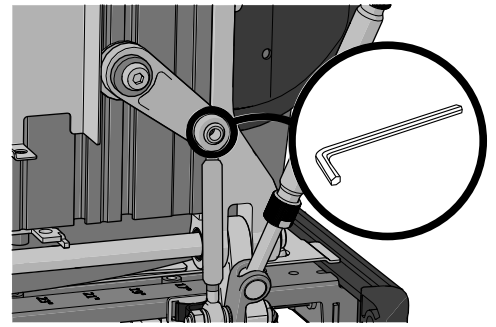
Das Gelenk für die Schiebefunktion der Rückenlehne ist mit einer Schraube befestigt.
